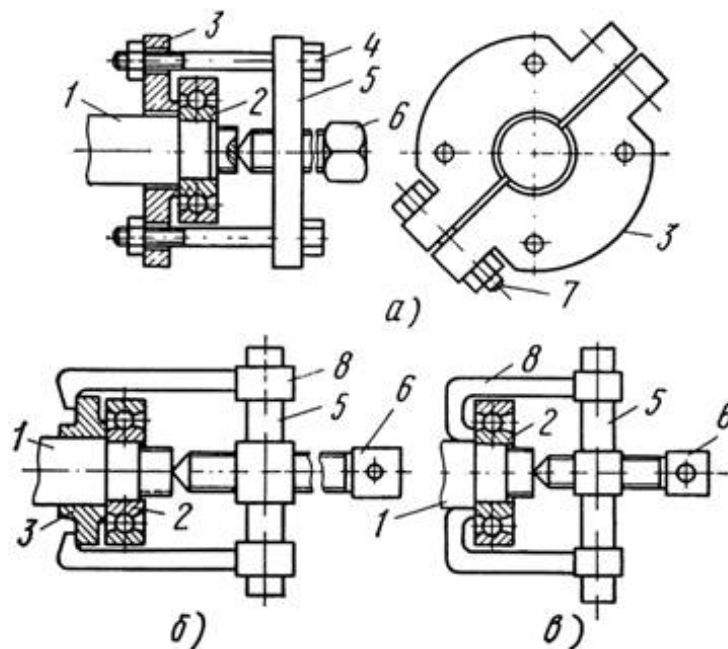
Приспособления для снятия подшипника с вала с помощью разъемного кольца и четырех стяжных болтов (а), разъемного кольца и винтового съемника (б) и винтового съемника (в):
